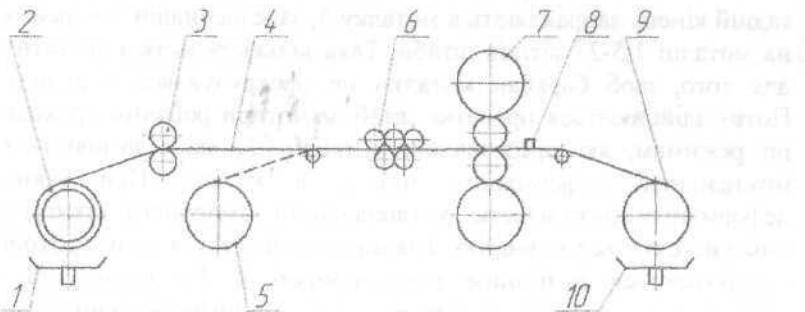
Схема реверсивного чотирьохвалкового стана: 1 – стіл; 2 – розмотувач; 3 – тягнучі ролики; 4 – штаба; 5 – моталка; 6 – роликова проводка; 7 – кліті; 8 – вимірювач товщини штаби; 9 – моталка; 10 – прибиральний пристрій.
